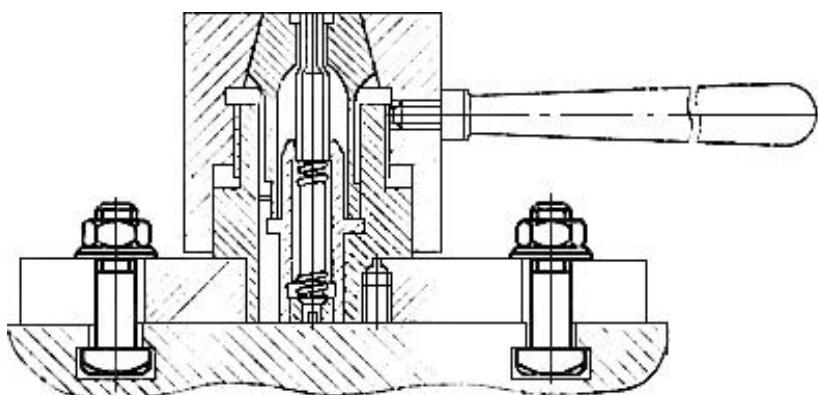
Пример применения Т-образных болтов, гаек и шайб для крепления приспособления
